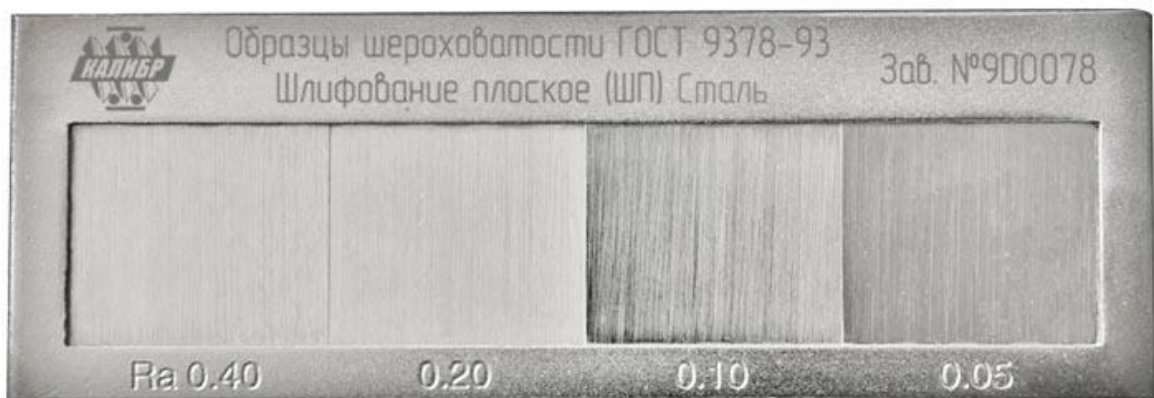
Общий вид образцов шероховатости в наборе из 4 штук в неразборной обойме
